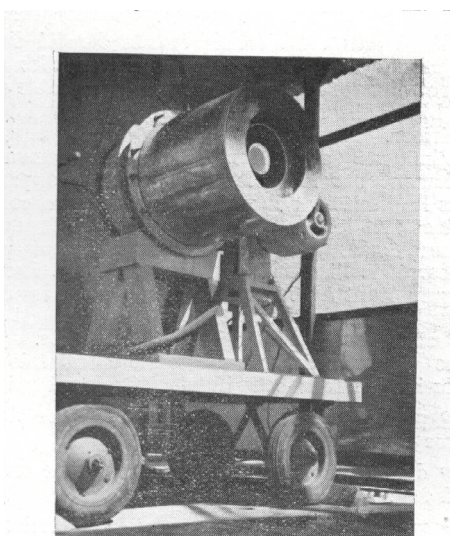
Vue rapprochée du four centrifuge précédent.
